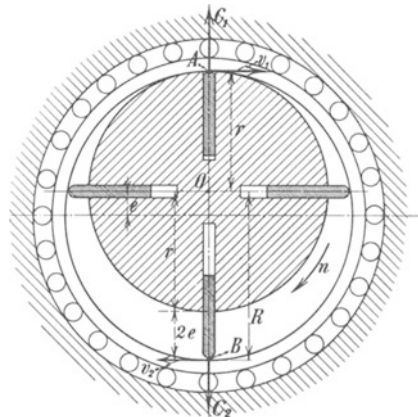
Aufnahme der Zentrifugalkräfte durch Ringe, auf Kugeln laufend.
